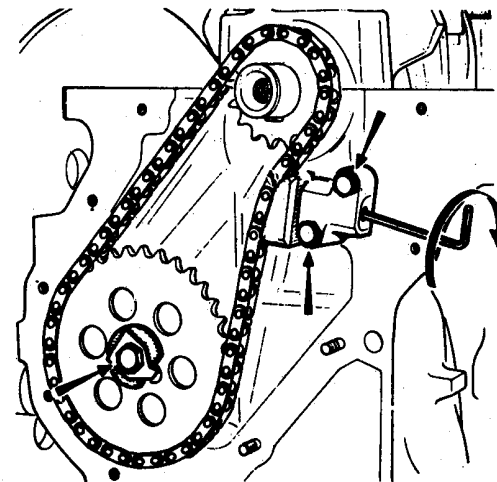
Fijación del engranaje del árbol de levas y colocación del tensor de la cadena.
